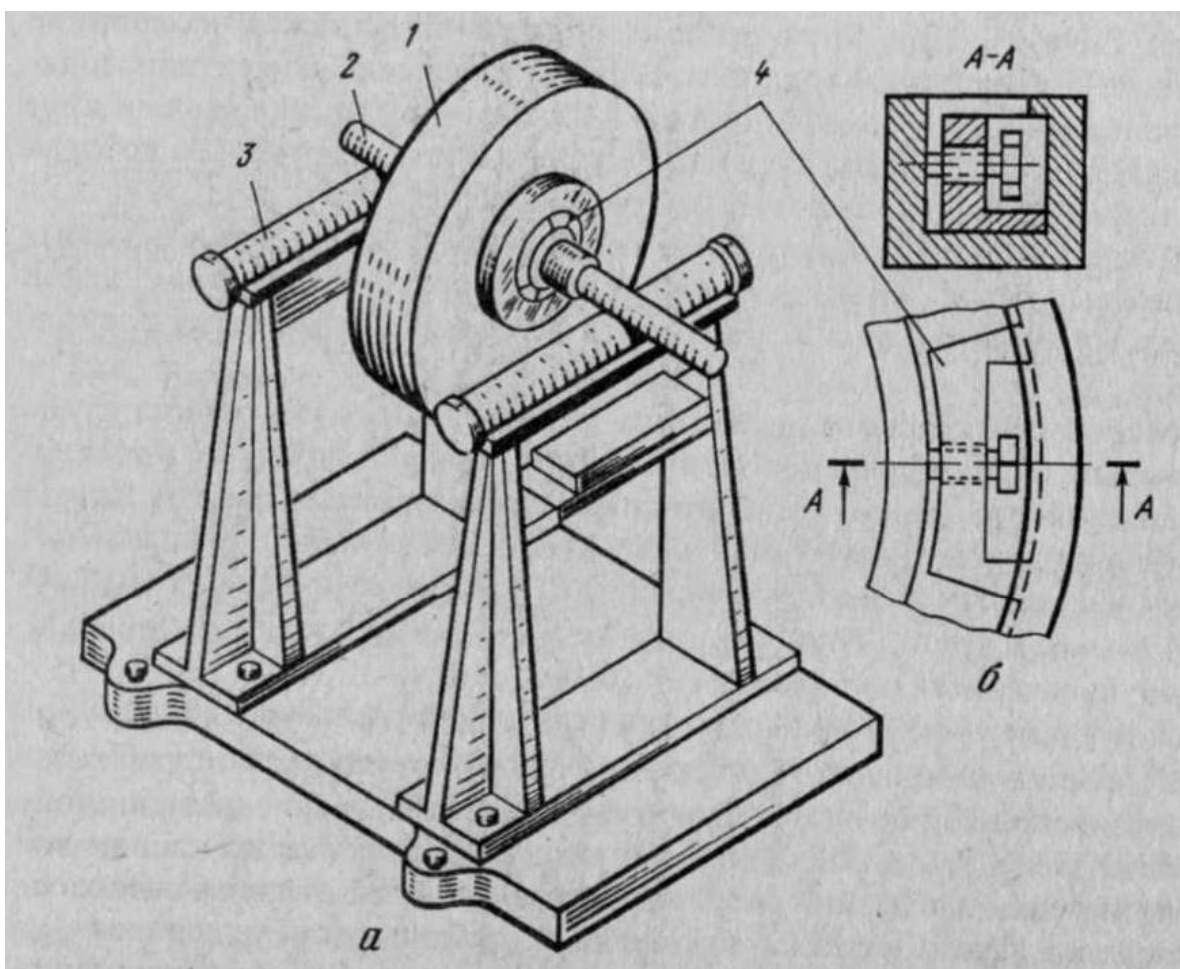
Стенд для статической балансировки шлифовальных кругов: а – вид со шлифовальным кругом и балансировочной оправкой, б – балансировочный сухарь - грузик, 1 – круг, 2 – балансировочная оправка. 3 – параллельные валики, 4 – сухари – грузики.
